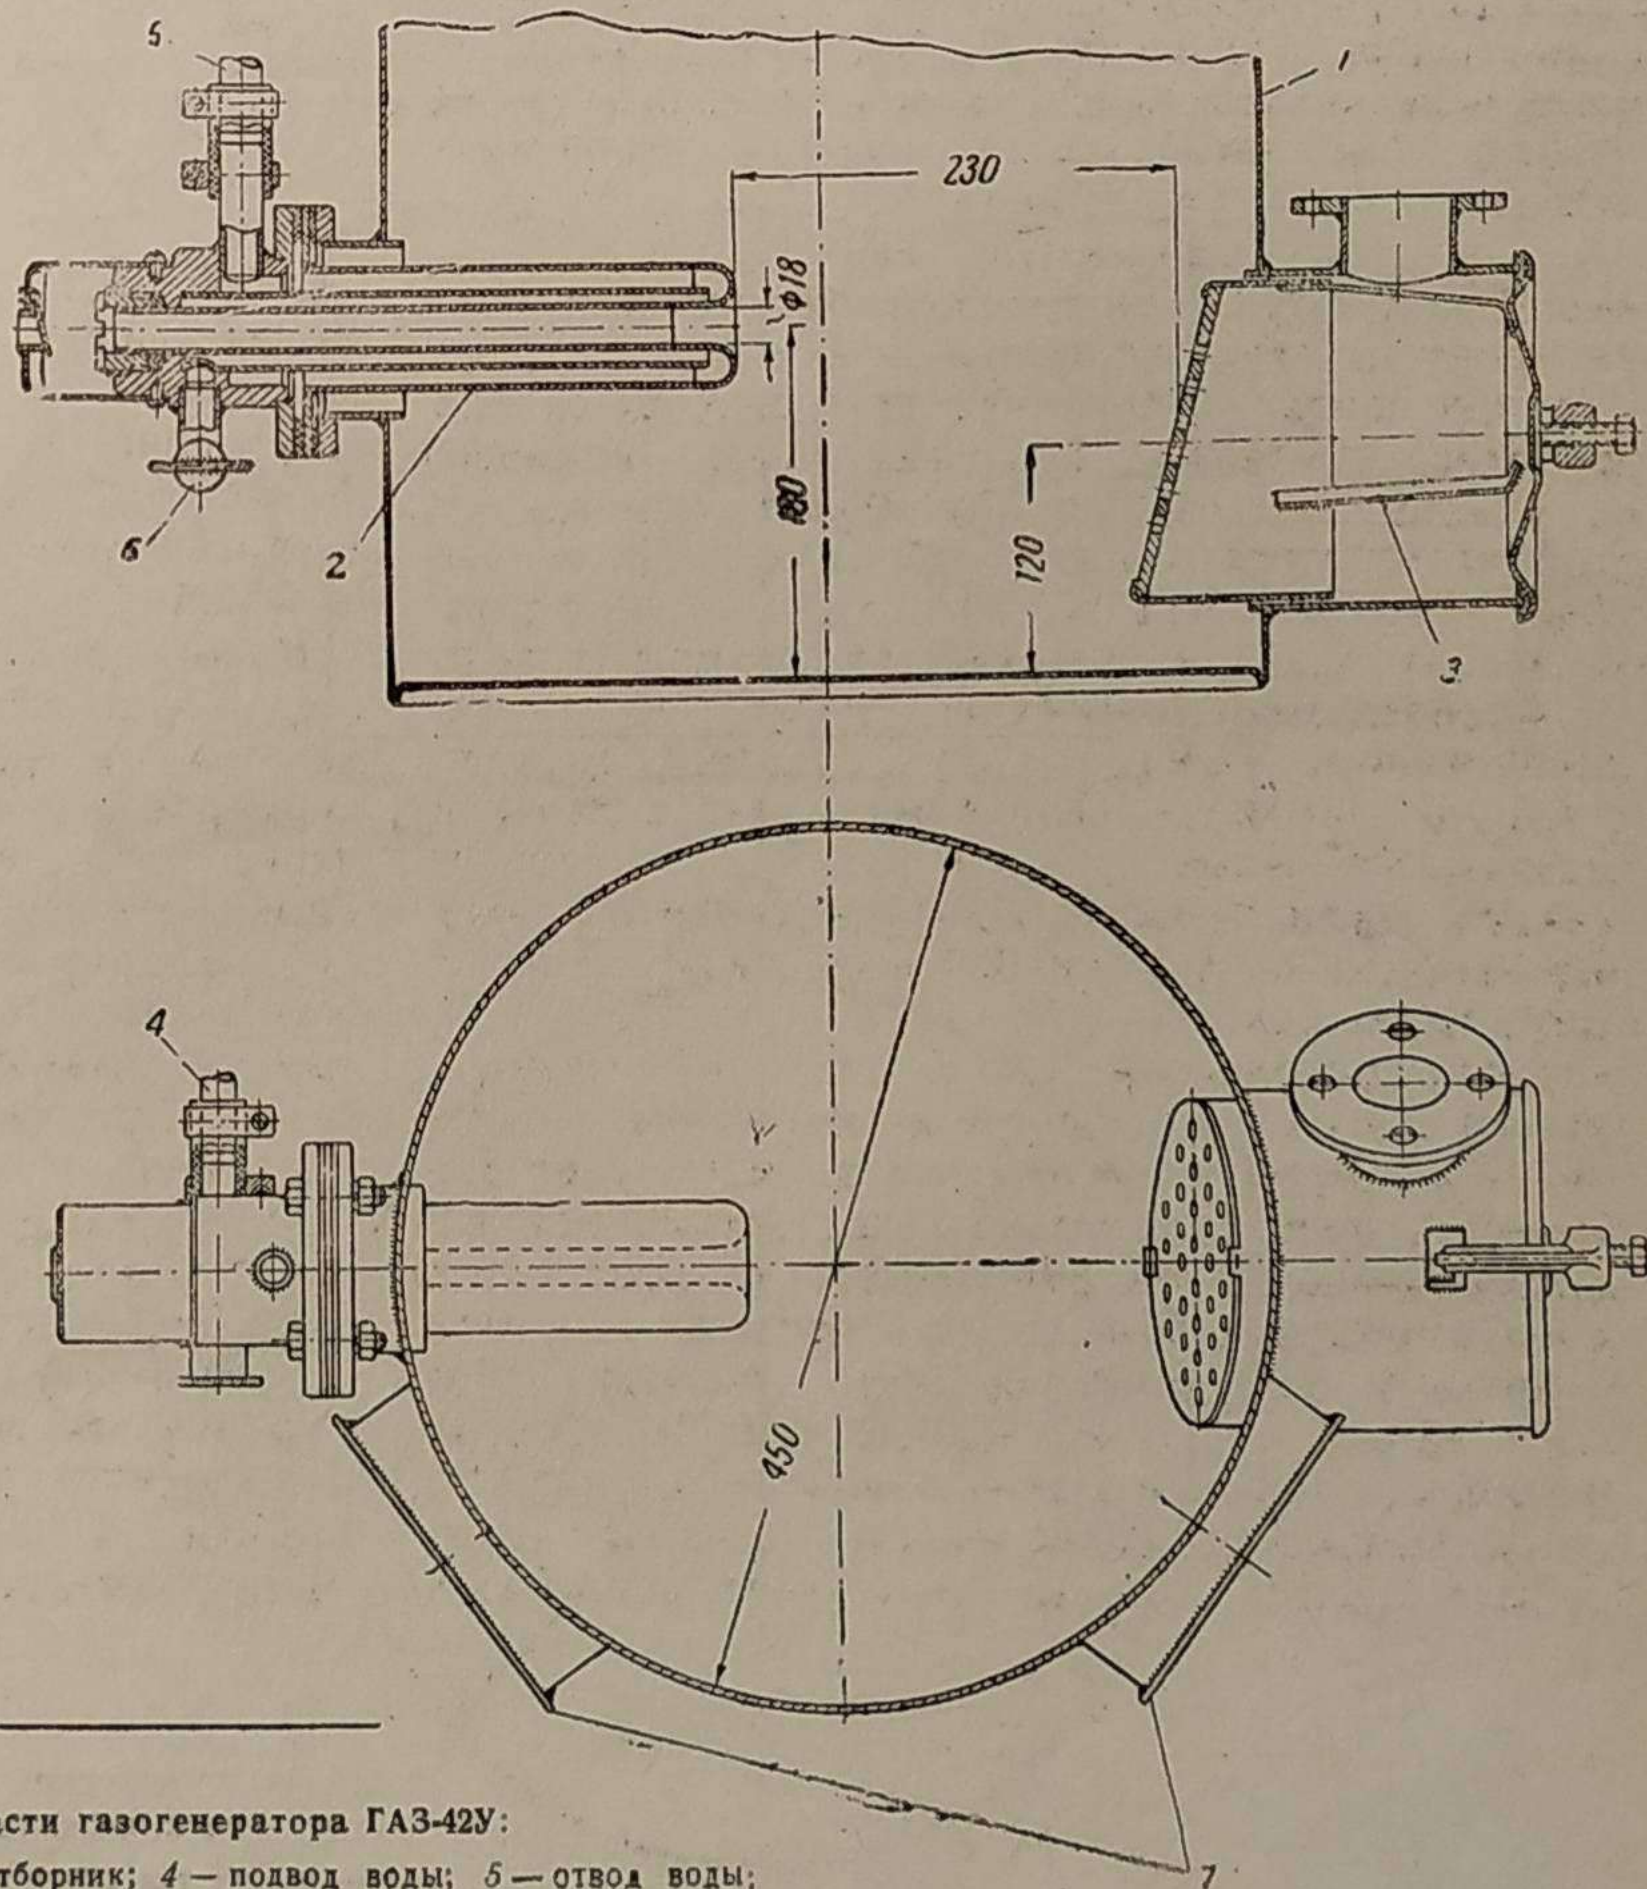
Общий вид нижней части газогенератора ГАЗ-42У:
